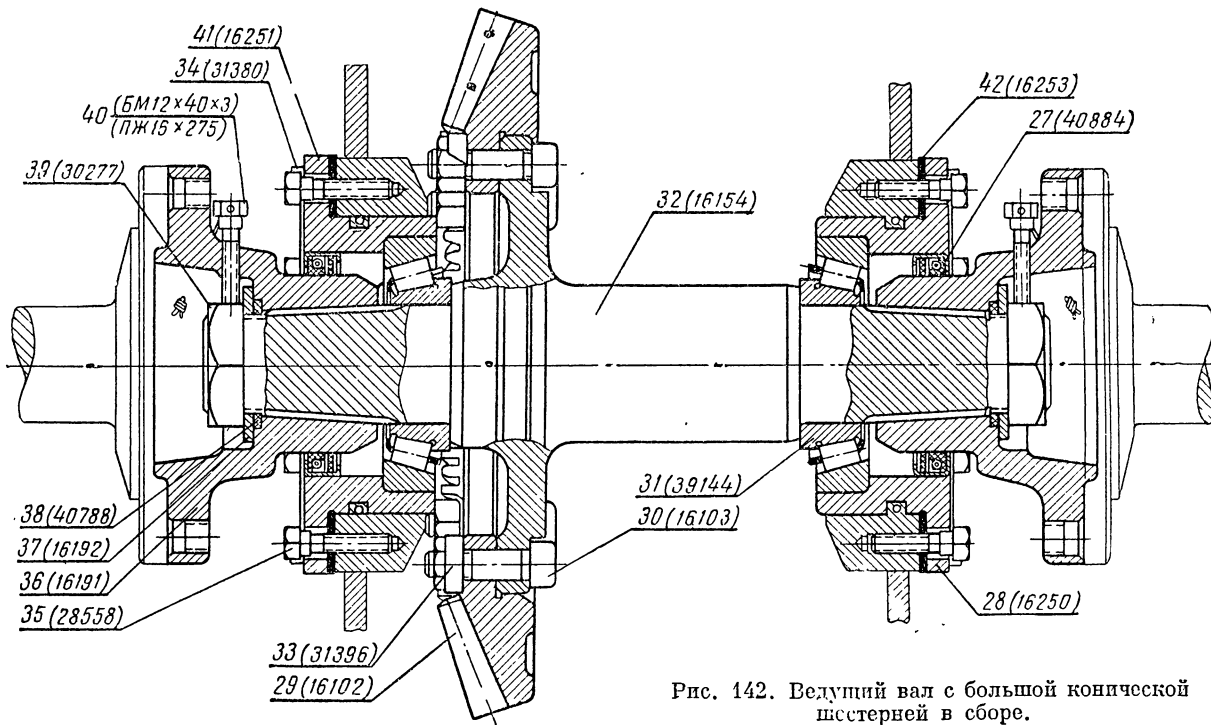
Ведущий вал с большой конической шестерней в сборе.
